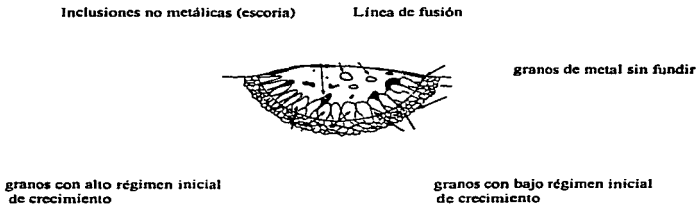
(d). SECCION TRANSVERSAL DE SOLDADURA CON INCLUSIONES ATRAPADAS
